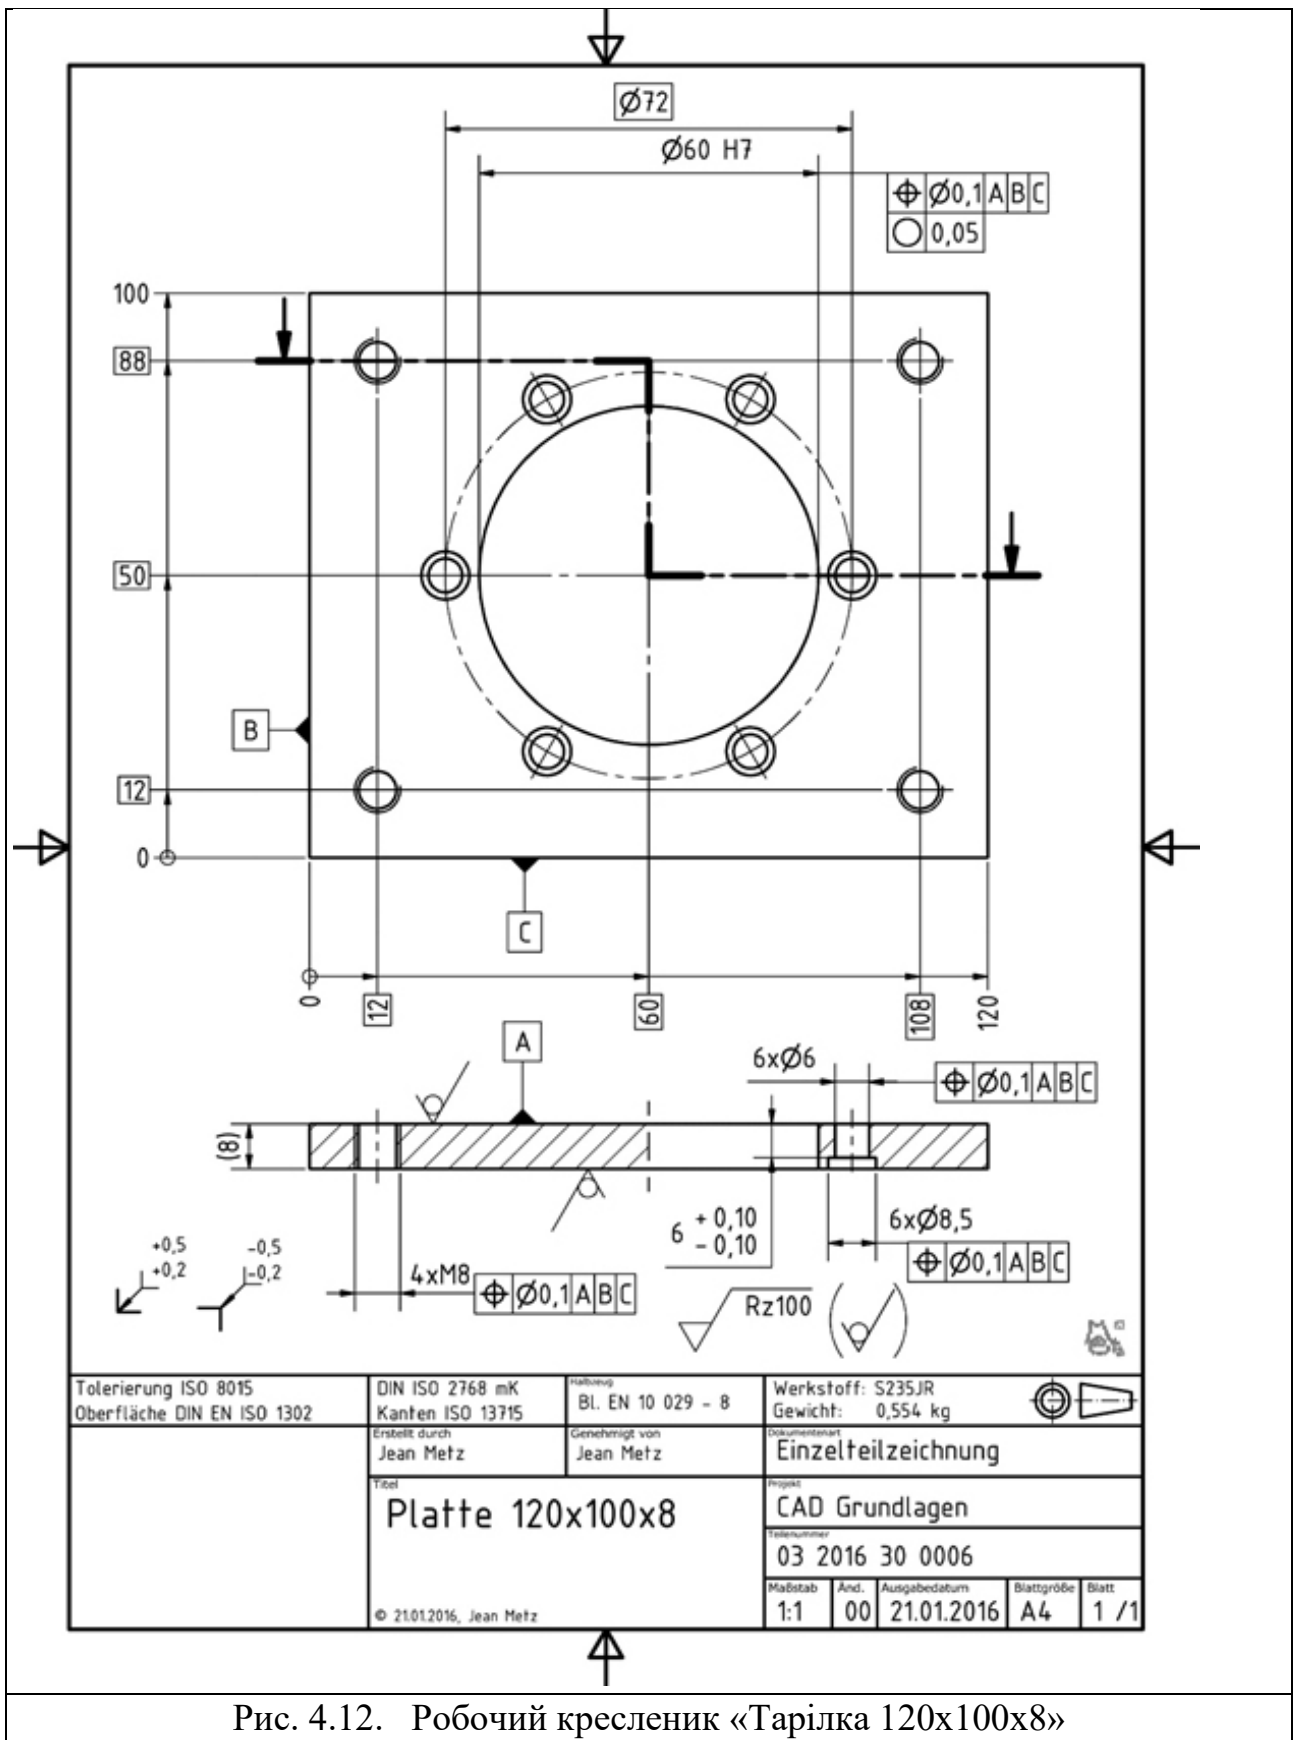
Робочий кресленик «Тарілка 120x100x8»
